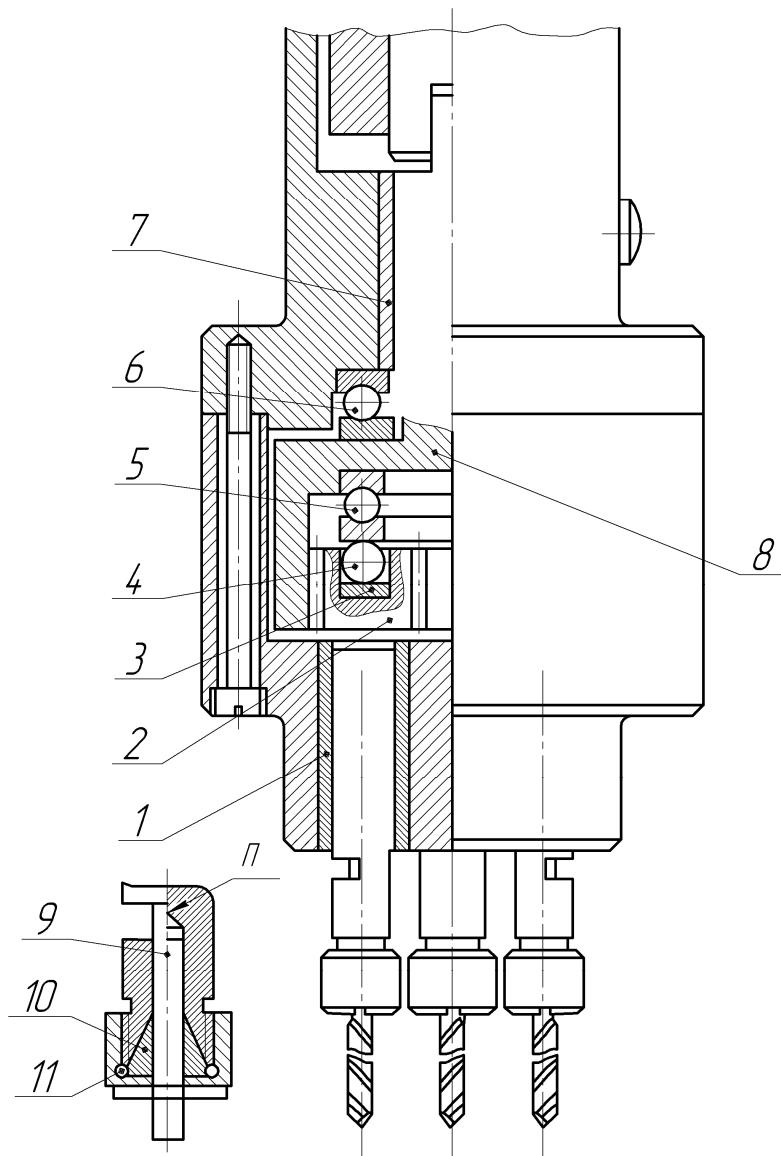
Будова багатошпindelної головки із зубчастими колесами внутрішнього зачеплення: 1 – втулка; 2 – зубчасте колесо; 3 – опора; 4 – кульки; 5, 6 – упорні підшипники; 7 – підшипник ковзання; 8 – валик; 9 – свердла; 10 – цанга; 11 – гайка
